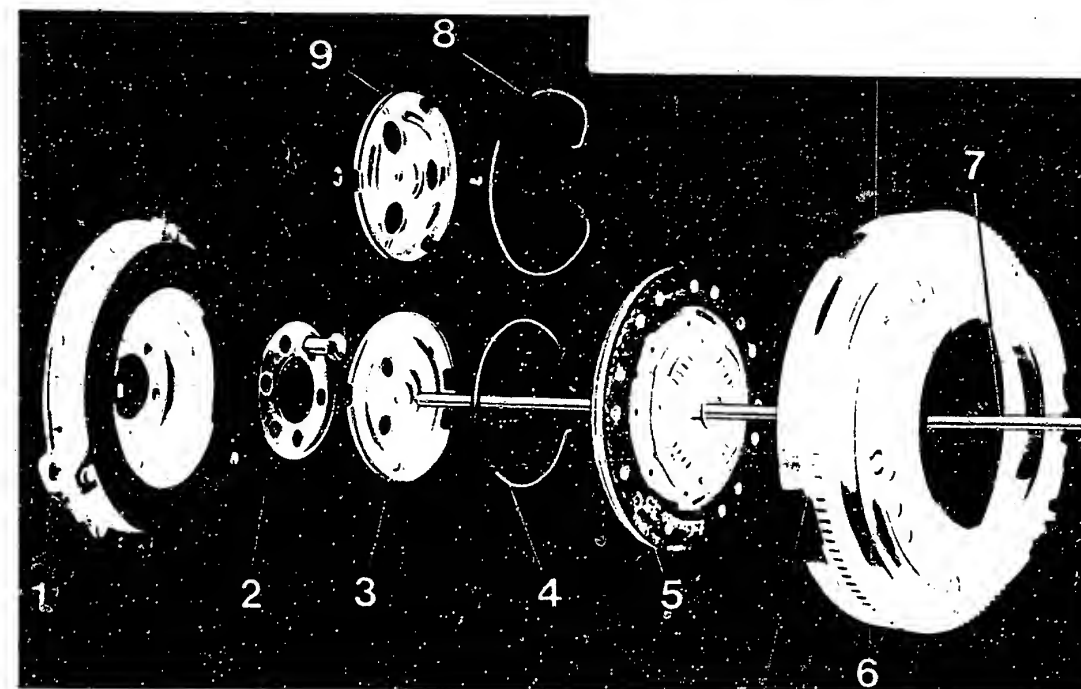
Kupplungsmechanismus der 1,6-l- und 1,8-l-Motoren – 1 Druckplattenträgerblech – 2 Zwischenblech – 3 Ausrückplatte – 4 Haltering – 5 Kupplungsscheibe – 6 Schwungrad – 7 Druckstange – 8 Haltering – 9 Ausrückplatte für stärkere Ausführung.
